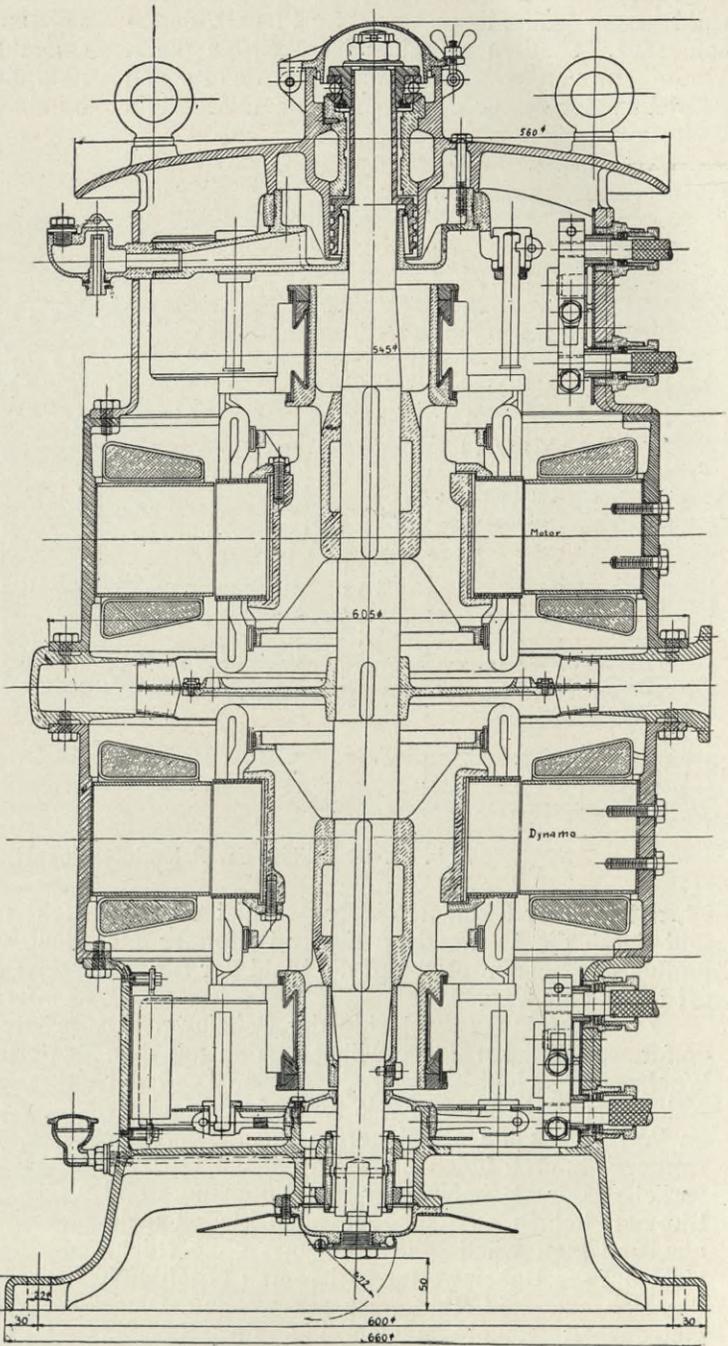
Scheinwerfermotorgenerator der Siemens-Schuckertwerke (Schnitt)
